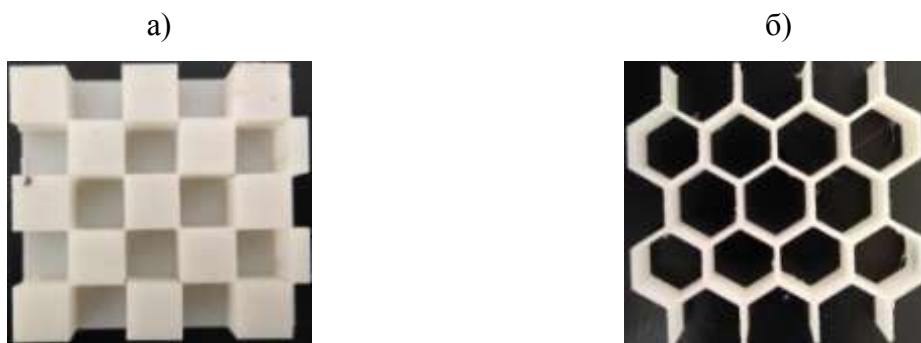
Общий вид образцов для испытаний на сжатие: а – складчатый наполнитель ЗПК; б – сотовый наполнитель ЗПК
